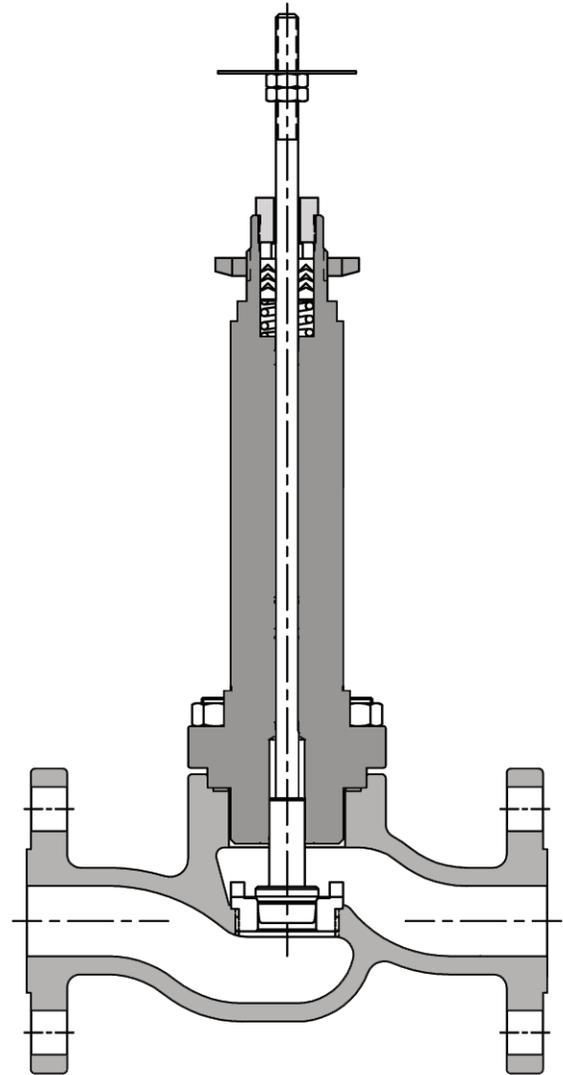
Корпус клапана 24000SVF в сборе с удлиненным штоком
